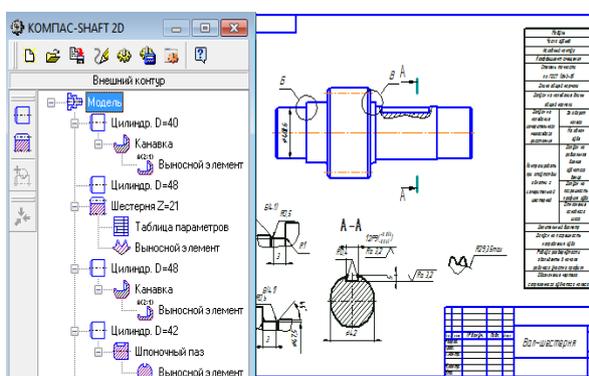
, а) – чертеж вала-шестерни, построенный с использованием приложения SHAFT-2D;
